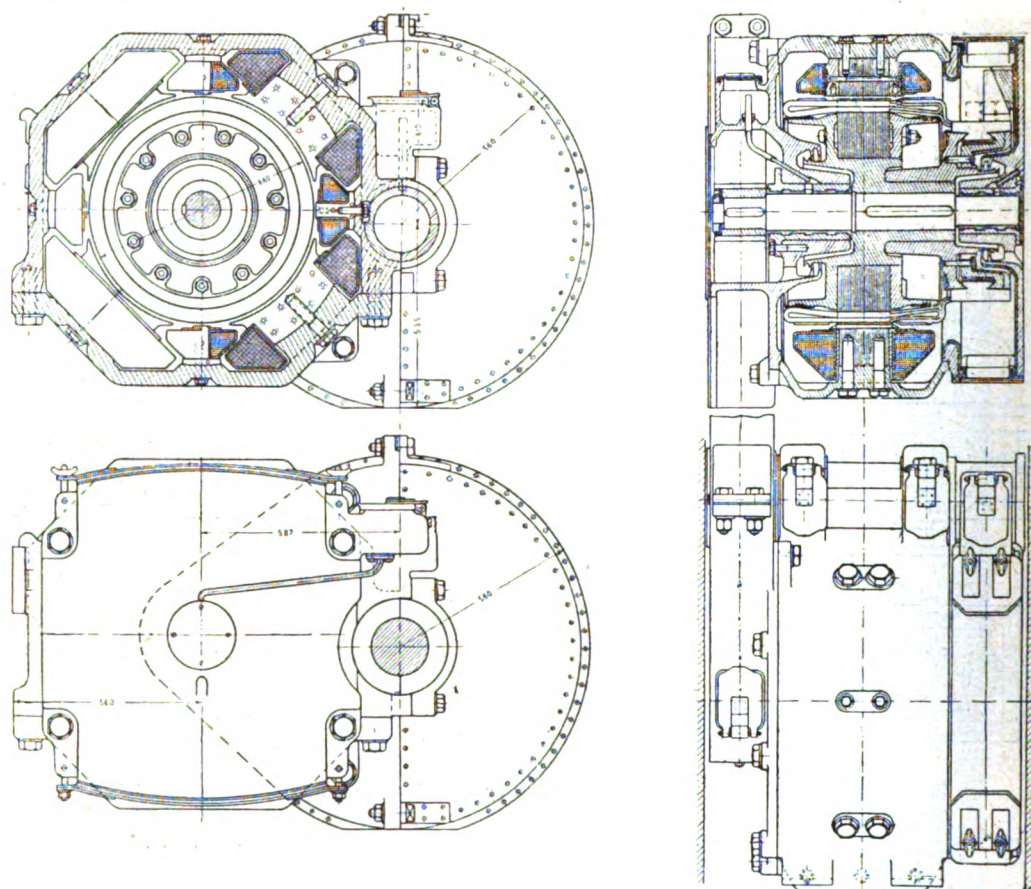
Vue et coupe du moteur de 160 H.P. à 2 000 volts.
